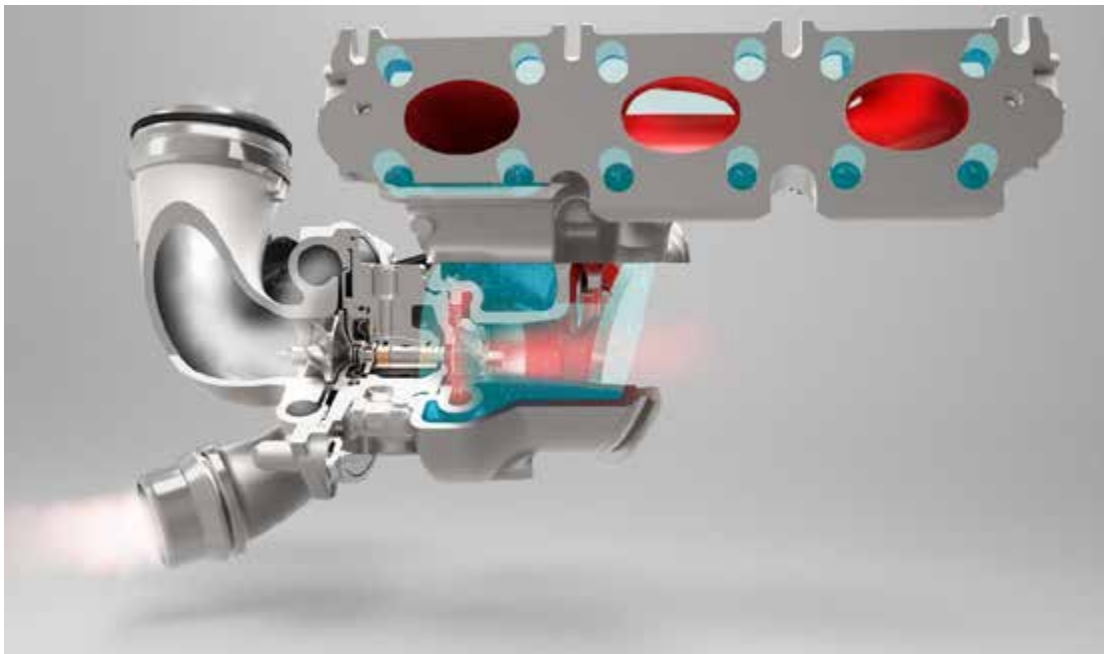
Современные турбокомпрессоры оснащены жидкостной рубашкой охлаждения, омывающей не только центральную часть, в которой установлены подшипники, но и корпус турбины, предотвращая чрезмерный нагрев деталей, и увеличение продолжительности жизни турбокомпрессора; источник: *Continental Corporation
